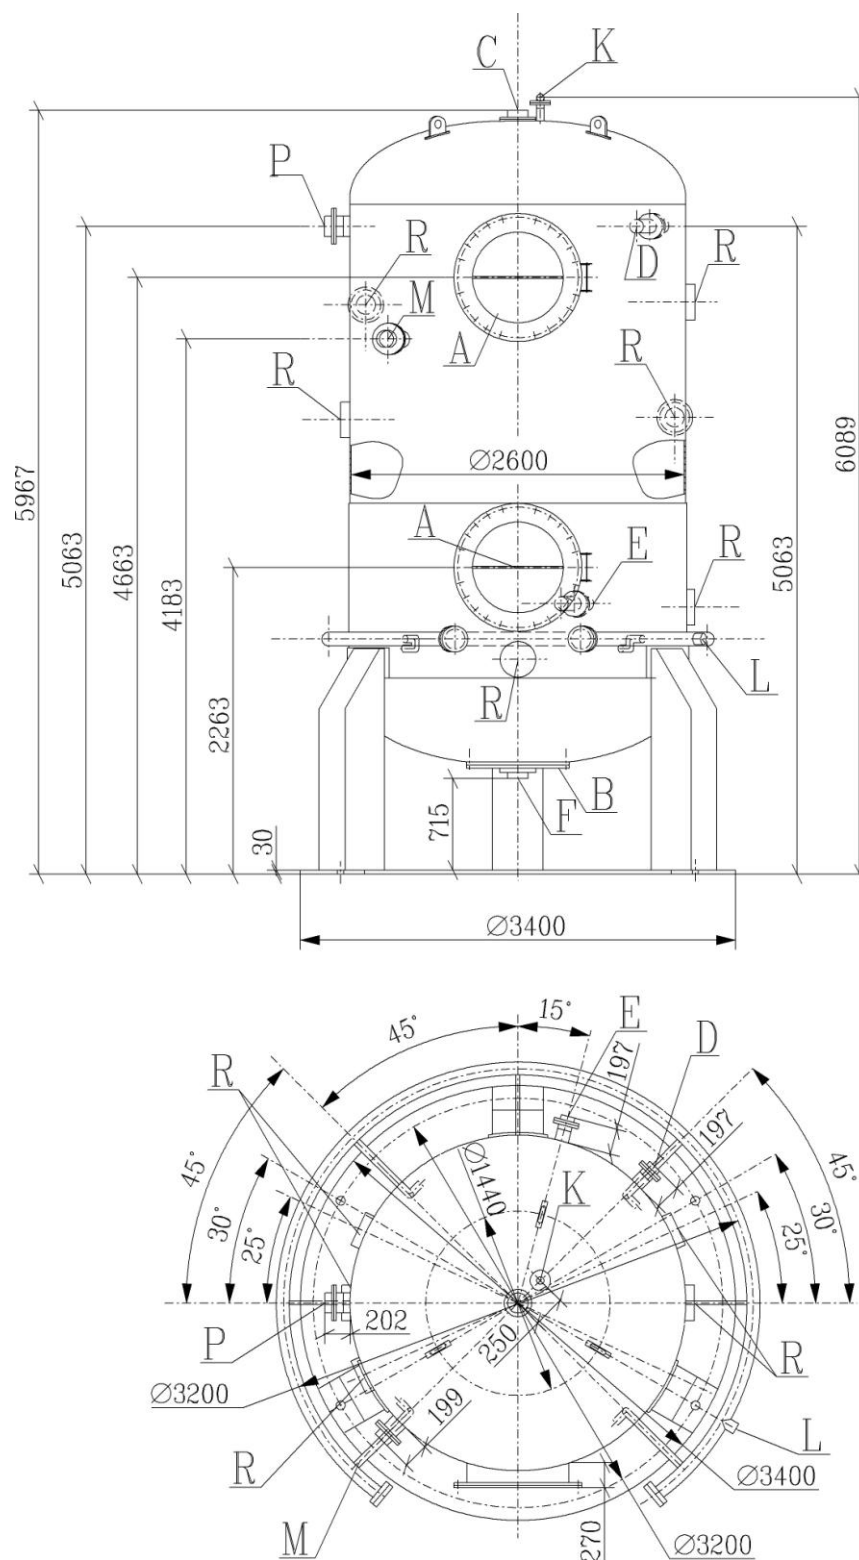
Габаритный чертеж фильтра-регенератора анионита LDP42AT001
